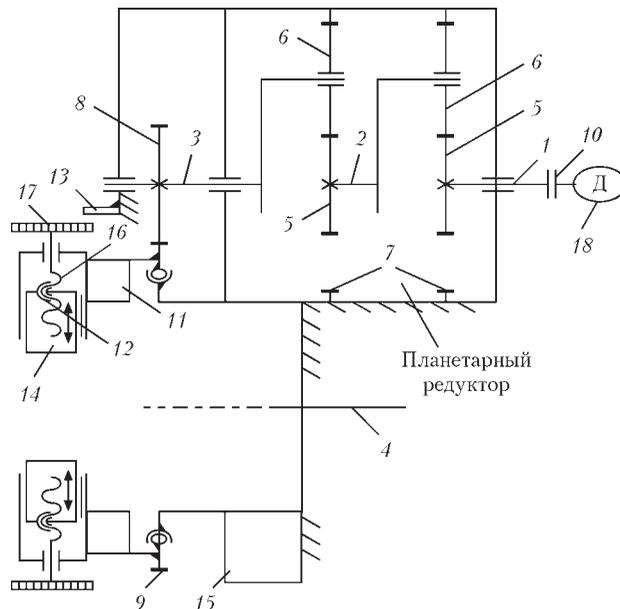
Кинематическая схема трубореза ТТЦ 660 У3.1: 1–4 — валы кинематических звеньев; 5–9 — шестерни кинематических звеньев; 10 — муфта; 11 — планшайба; 12 — гайка; 13 — фиксатор поворота; 14 — суппорт; 15 — корпус; 16 — винт ходовой; 17 — колесо зубчатое; 18 — пневмодвигатель
